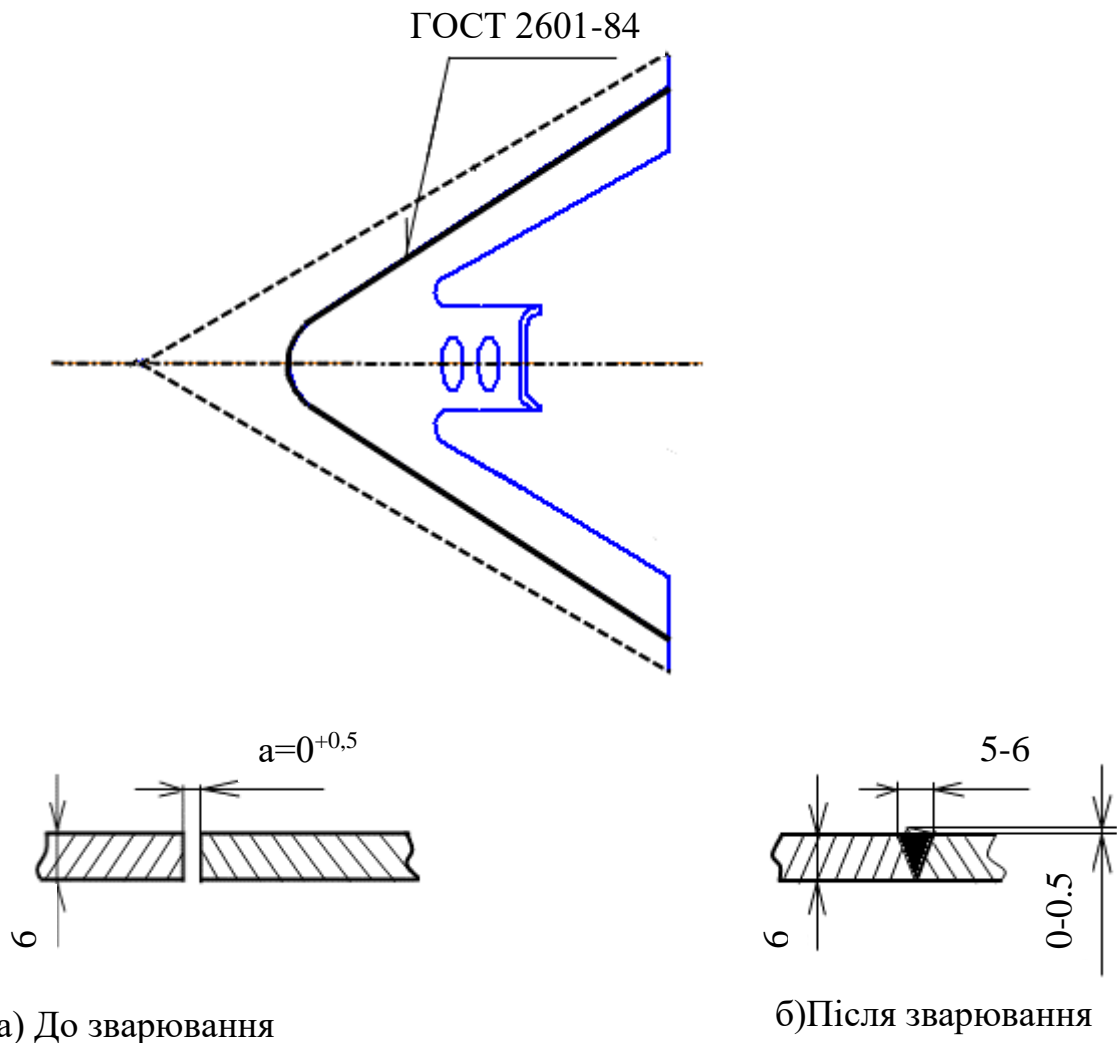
Схема підготовки кромки перед зварюванням та зварне з'єднання.
